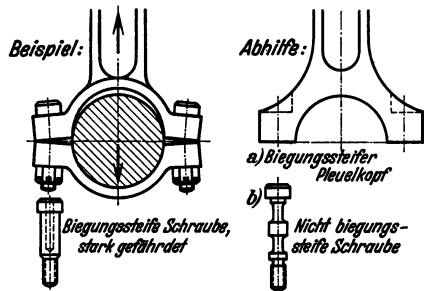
Richtige Formgebung von Pleuelstangenkopf und Schrauben. Große Dehnlänge der Schrauben kann die aufgezogenen Verformungen aufnehmen.
